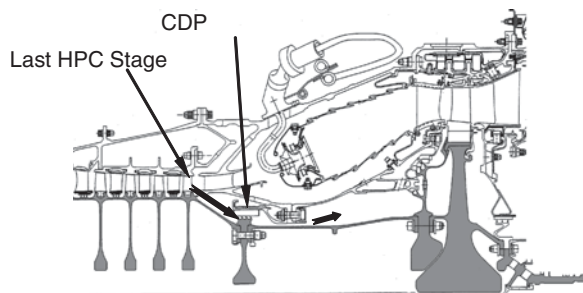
Das CDP Seal hinter dem Verdichteraustritt. (© CFM)
